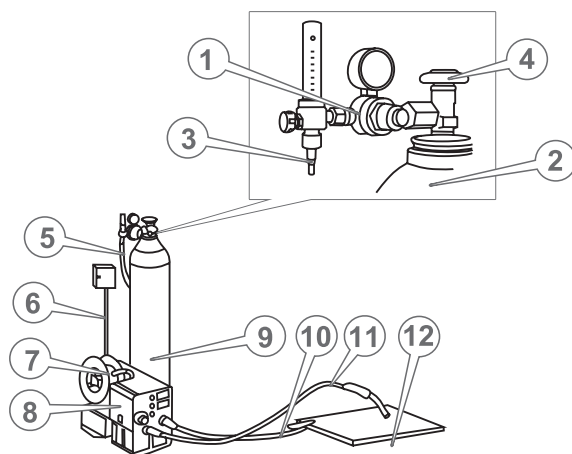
Схема під'єднання обладнання для роботи в режимі напівавтоматичного дугового зварювання із використанням середовища захисного газу.
